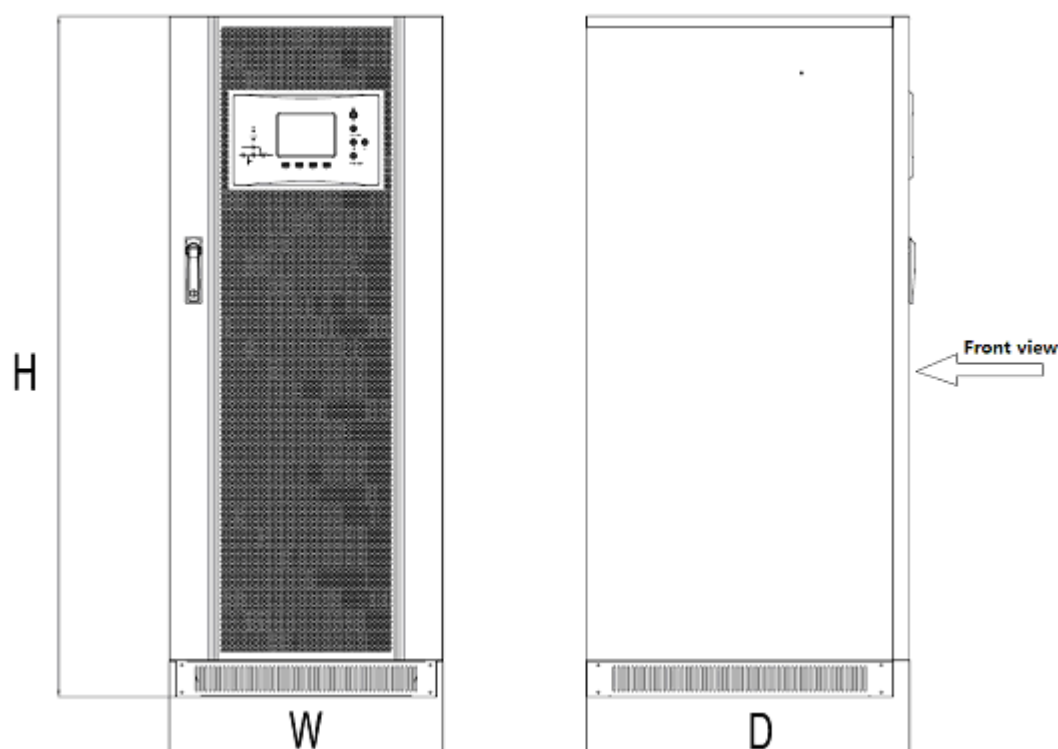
Внешний вид моделей 60~120кВА [H=высота, W=ширина, D – длина, Front view=фронтальный вид]
